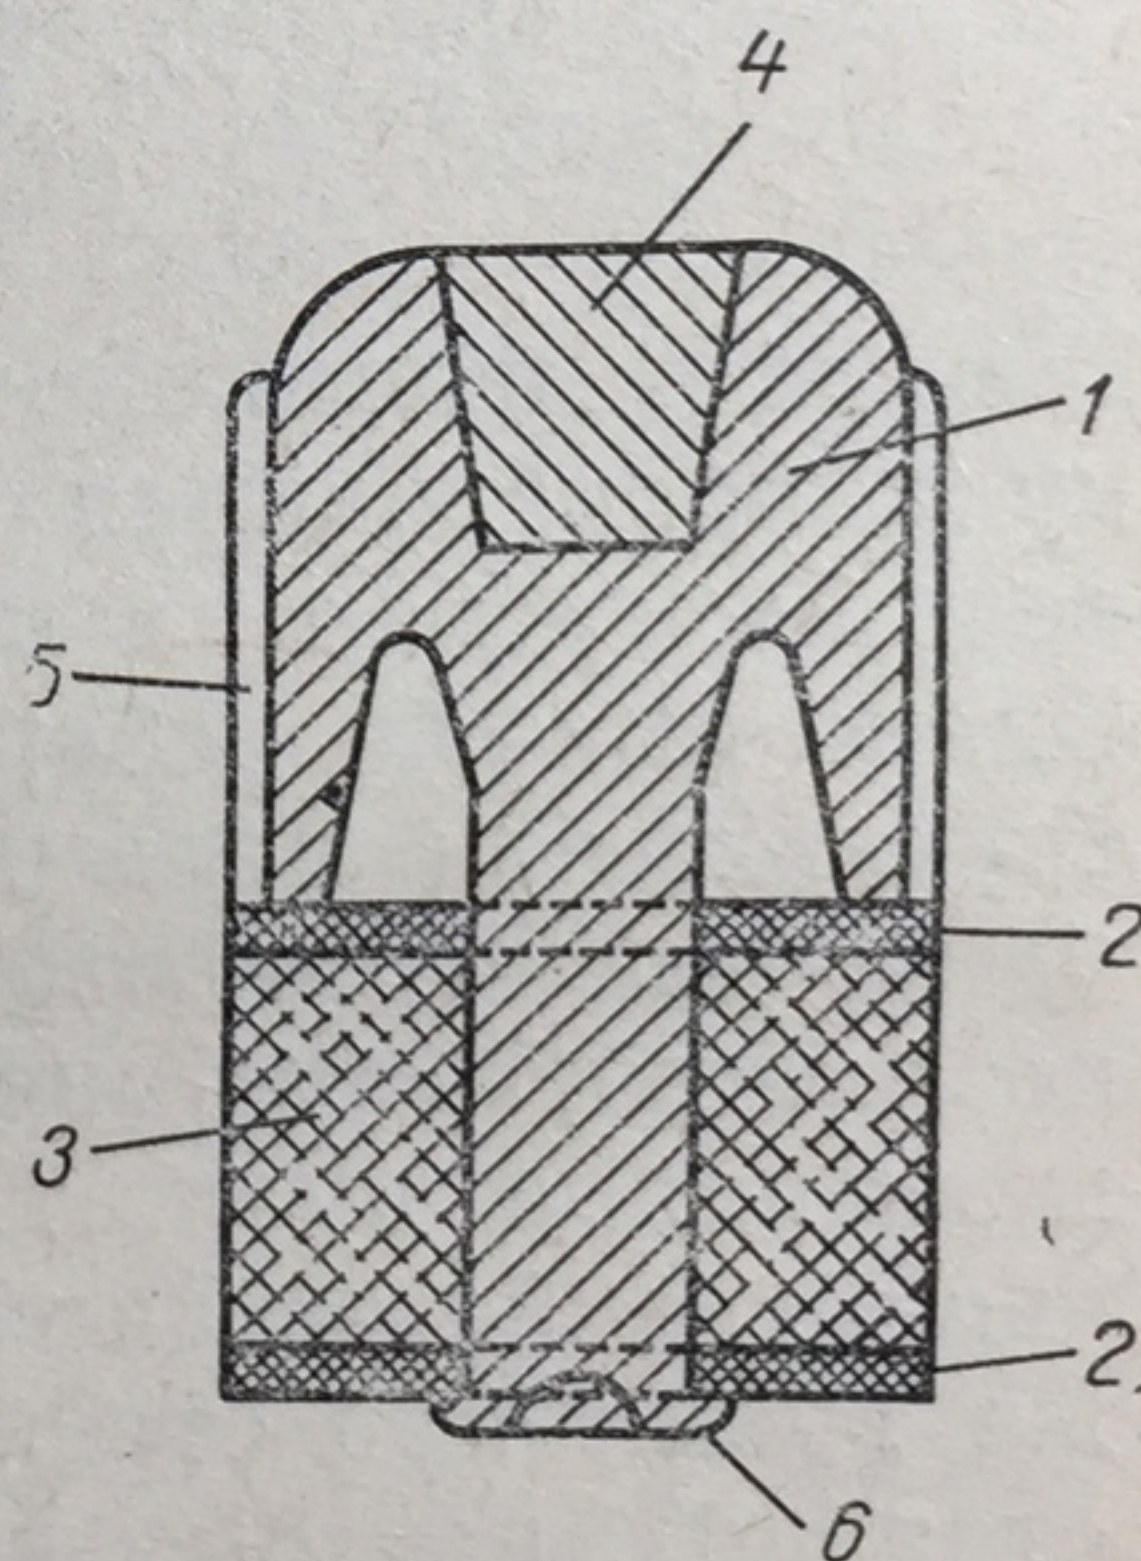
Устройство пули Якана на разрезе. 1 — свинцовый корпус; 2 — картонные прокладки (пыжи); 3 — войлочный пыж; 4 — свинцовая пробка, заполняющая экспрессную пустоту; 5 — ведущие ребра; 6 — свинцовый хвостовик.
